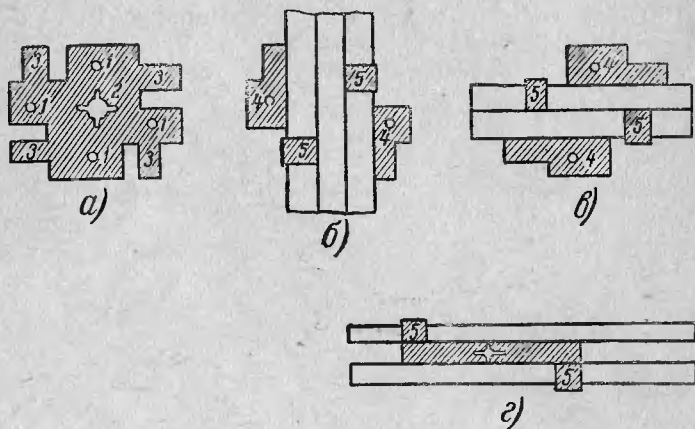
Крепежные пластинки для крепления плоских проводов.
